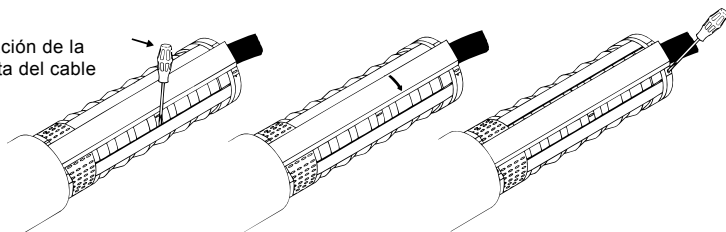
Desmontaje e instalación de la cubierta del cable para bombas SP 35S, 45S, 62S, 77S, 150S, 230S, y 300S
